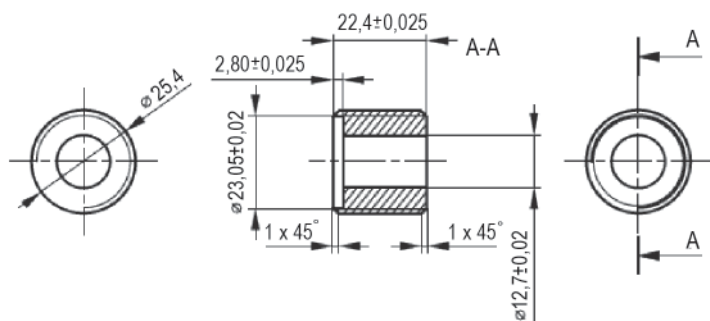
Деталь 7 – Приспособление для разборки
